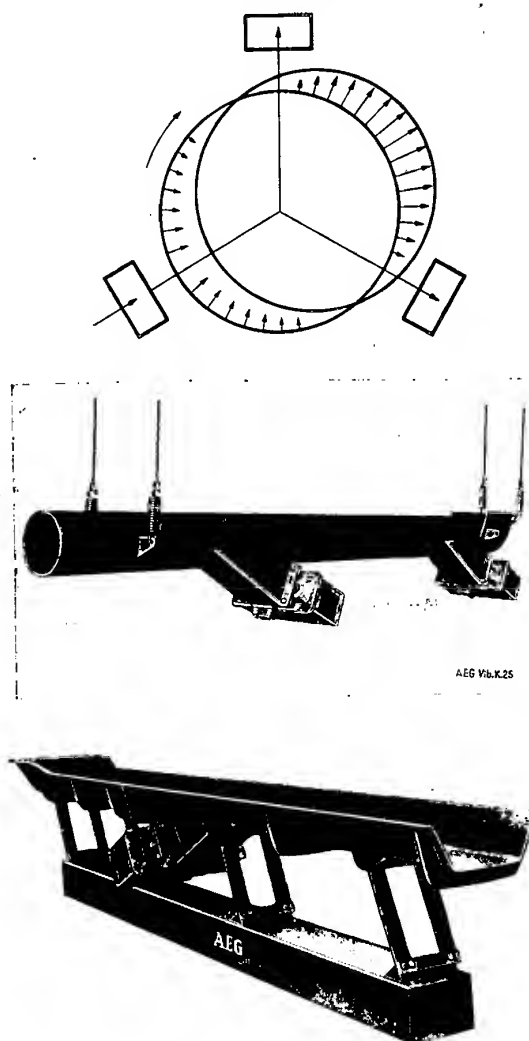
Technische Ausführungsformen von Schwingantrieben:
